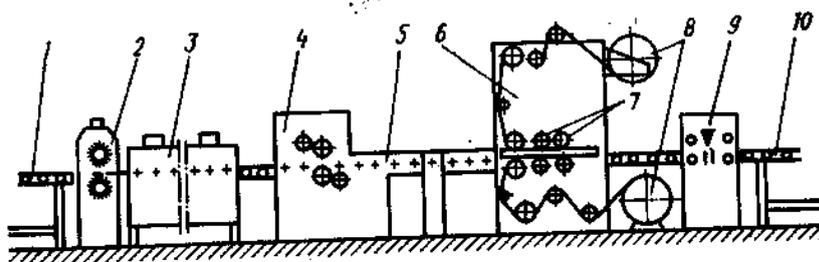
Схема линии кэширования: 1 — роликовый конвейер; 2 — щеточный станок; 3 — камера предварительного обогрева; 4 — клеенаносящий станок; 5 — конвейер выдержки; 6 — облицовочный (кашировальный) станок; 7 — прикатывающие валы; 8 — рулоны бумаги; 9 — отрезное устройство; 10 — приемный роликовый конвейер
